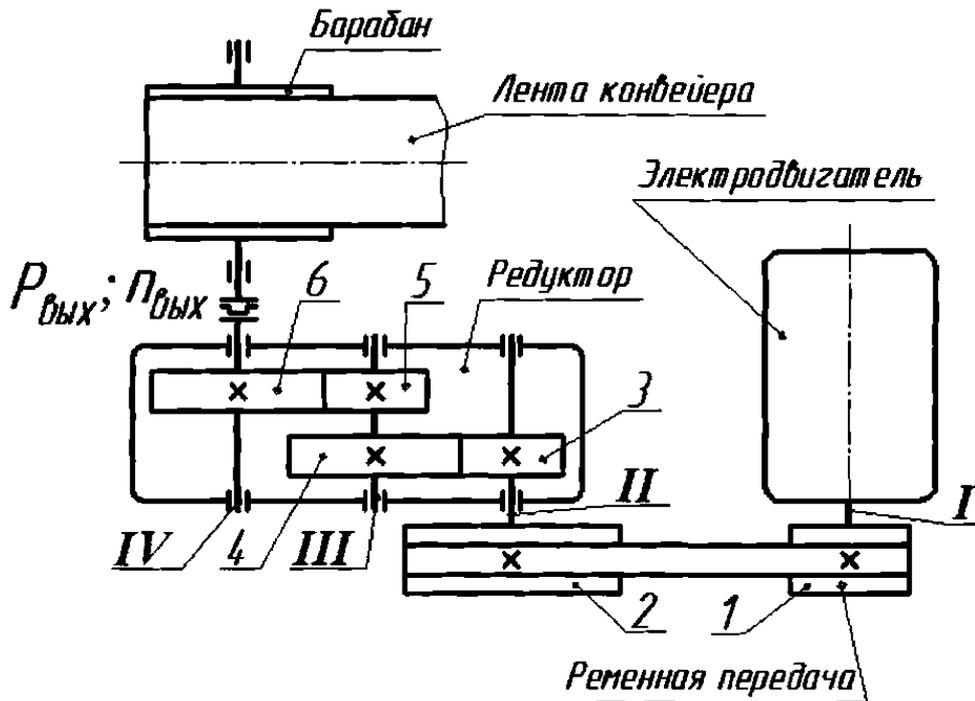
Кинематическая схема привода с развернутым цилиндрическим редуктором (Схема № 1).
